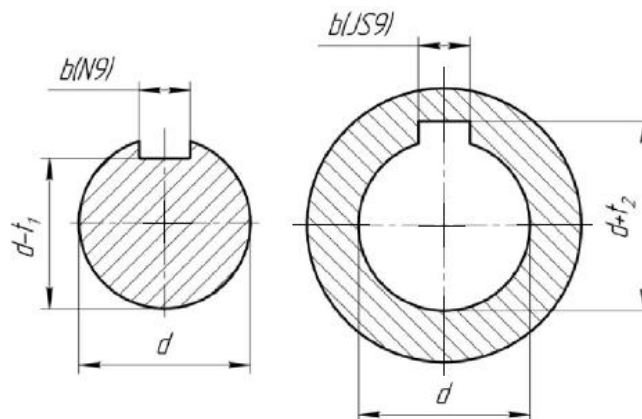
Поля допусків шпонкових пазів вала та втулки
